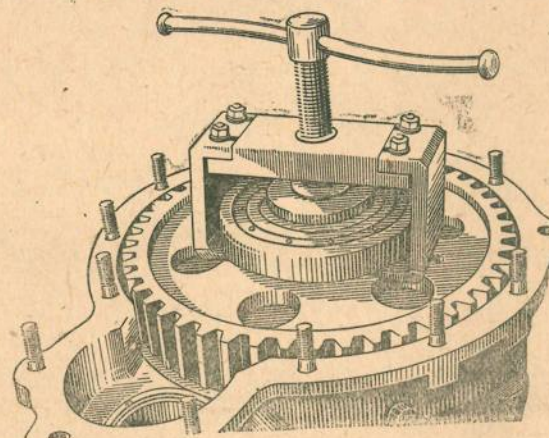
Снятие шарикоподшипника со ступицы ведомой шестерни при помощи приспособления
